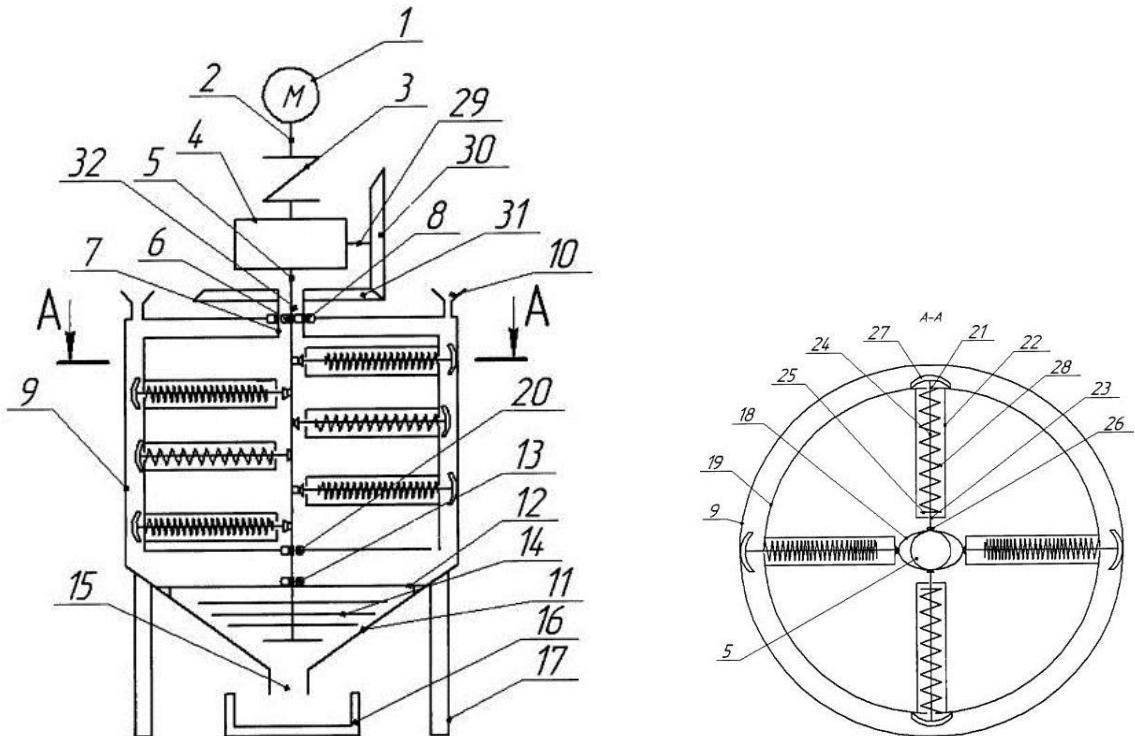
Устройство для дробления зерна (Патент РФ №2742055)
